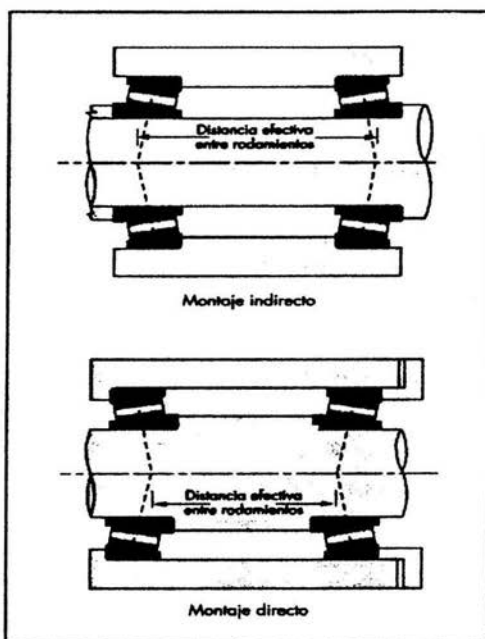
Formas de montaje de rodamientos de una hilera de rodillos cónicos
